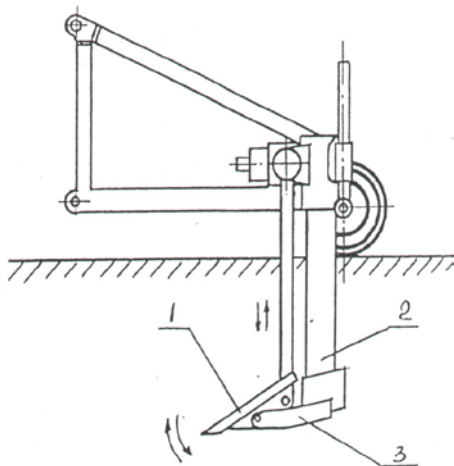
Схема вібраційного розпушувача: 1-зубило; 2-стовба; 3– пята.
